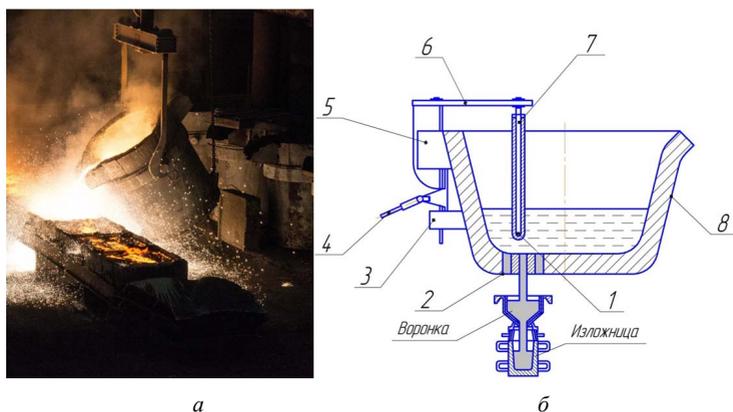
Разливочный ковш: *a* – внешний вид (Рихаву); *б* – схема; 1 – пробка; 2 – стакан; 3, 5 – направляющие для тяги; 4 – рукоятка; 6 – траверса; 7 – стальной стержень; 8 – стальной кожух
